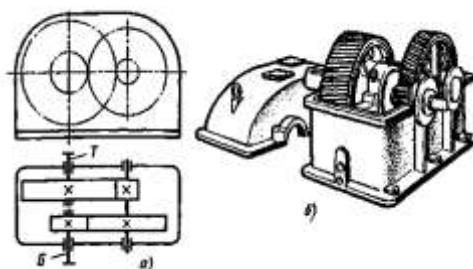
Двухступенчатый горизонтальный соосный редуктор:
